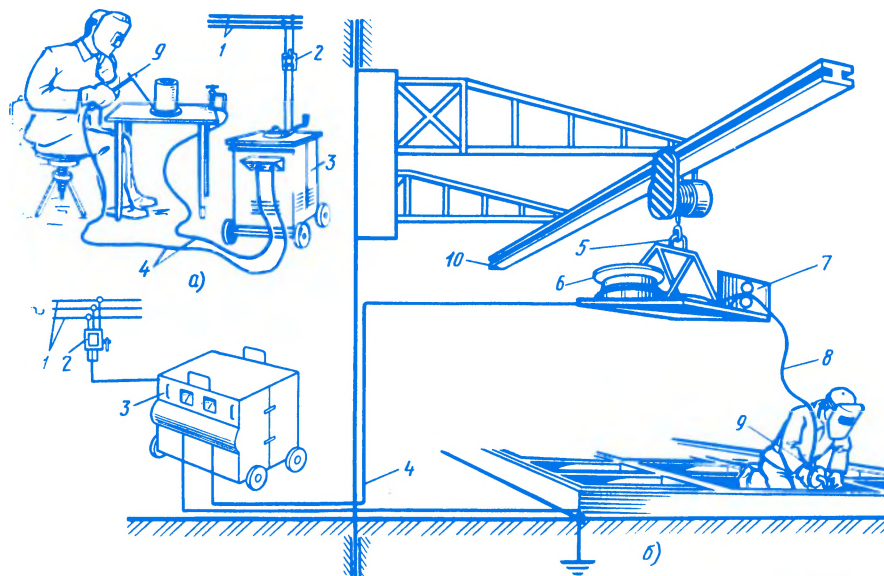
Сварочные посты для ручной и механизированной сварки:
